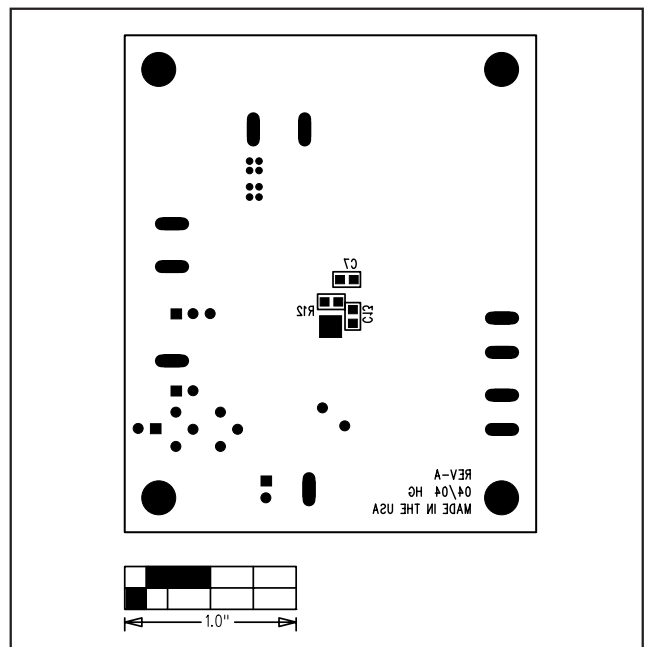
MAX1870A 评估板元件布局图 — 焊接面
